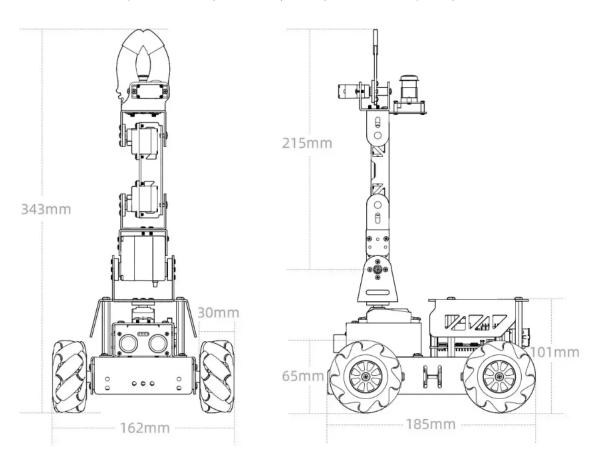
Габаритные чертежи робота-манипулятора МР.
